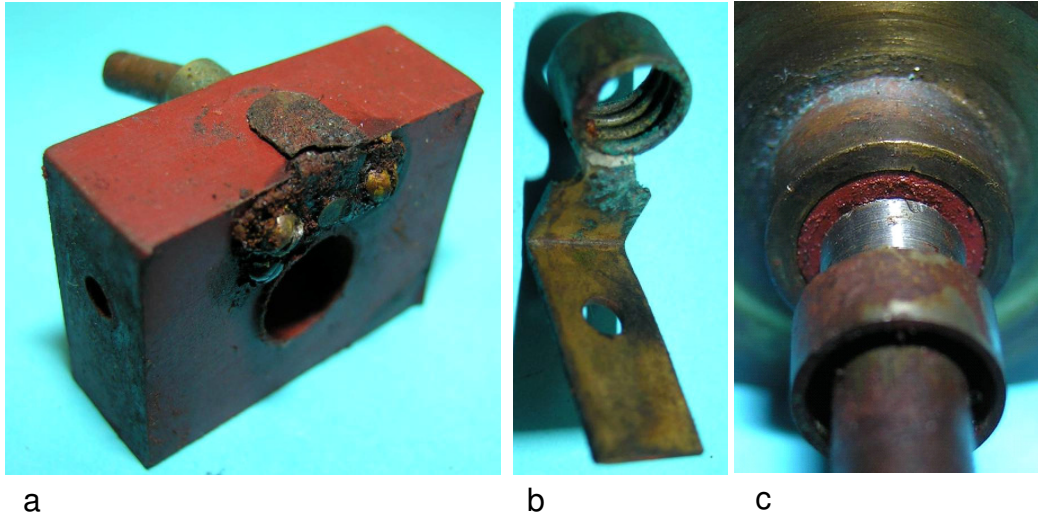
Kontaktblock und Läuferstabilisierung: a) Bürstenhalter und Fußkontakt für die Glühlampe, Bohrung zur Stabilisierung des Läufers, b) Fassung mit Masseblech, c) Ring zur Stabilisierung der Drehbewegung des Läufers
